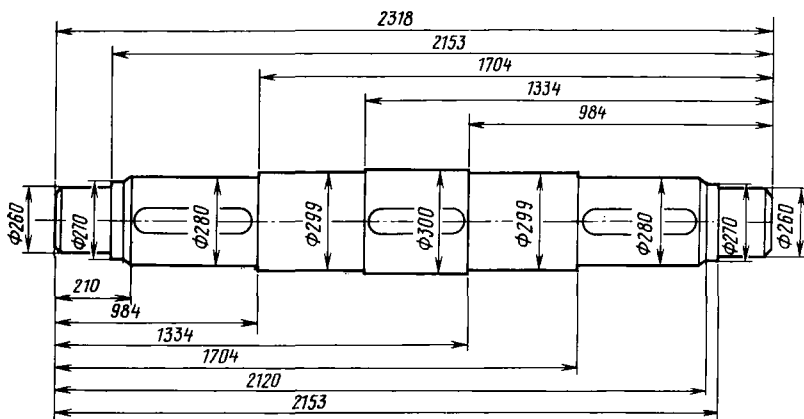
Главный вал главного редуктора эскалатора ЛТ-1
